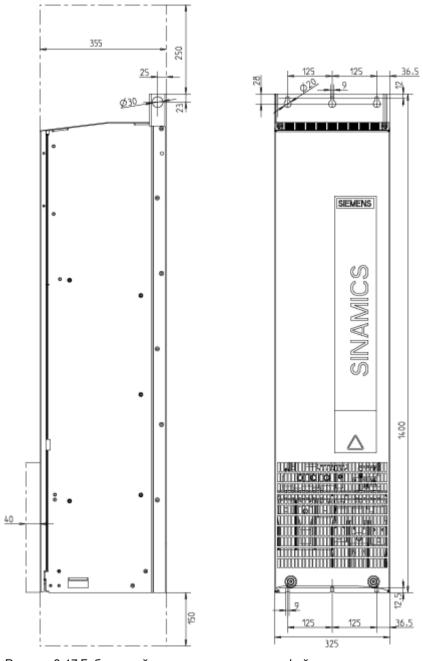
Габаритный чертеж активного интерфейсного модуля, типоразмер FI. Вид сбоку, вид спереди
